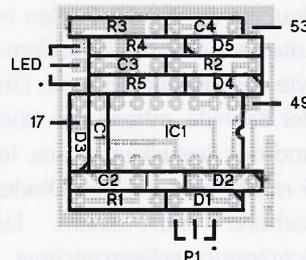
Der Bestückungsplan, hier mit dem gerasterten Layout hinterlegt
